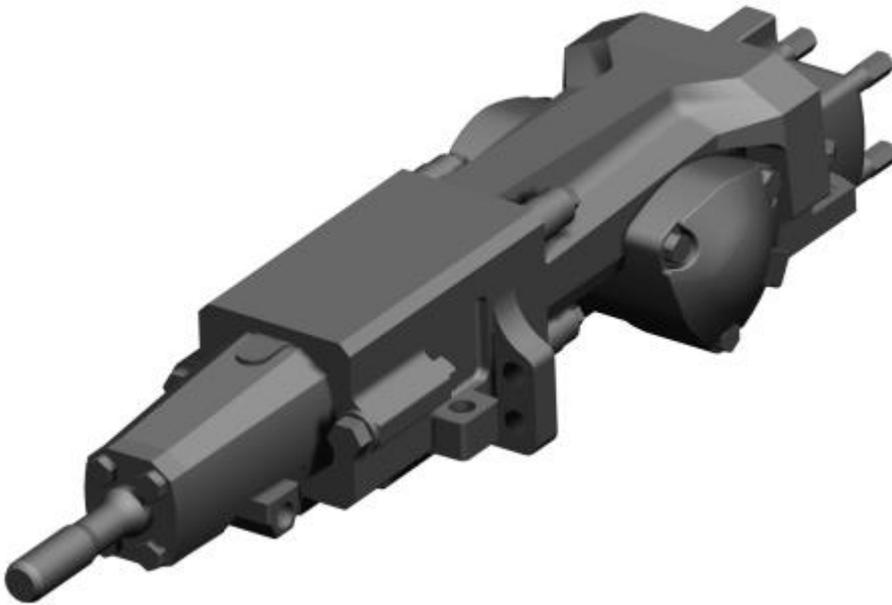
внешний вид гидроперфоратора SANDVIK HL510
